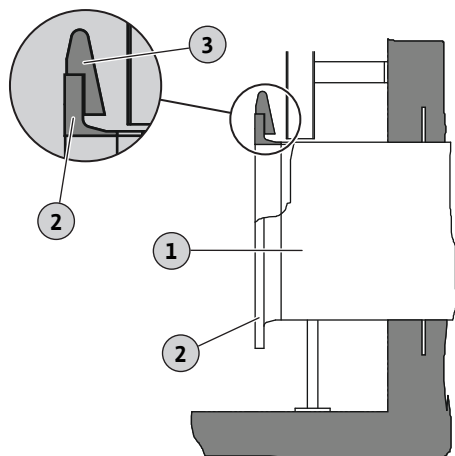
Andruckkeil: Druckrohr mit Vorschweißflansch
